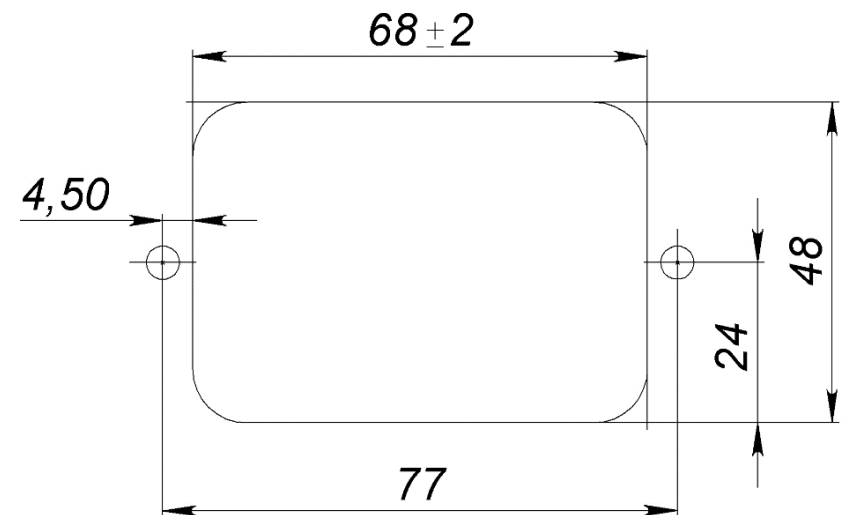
Разметка под установку видеокамеры EVM1-IPx
